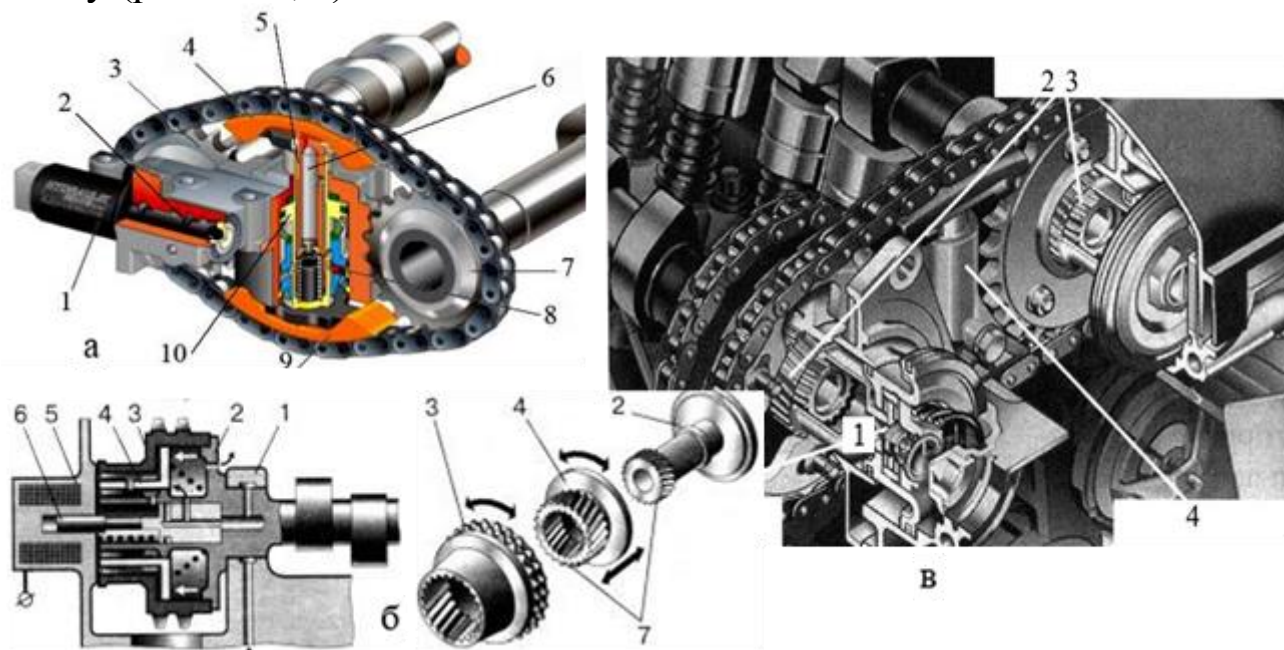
Пристрої для зміни фаз газорозподілу:
